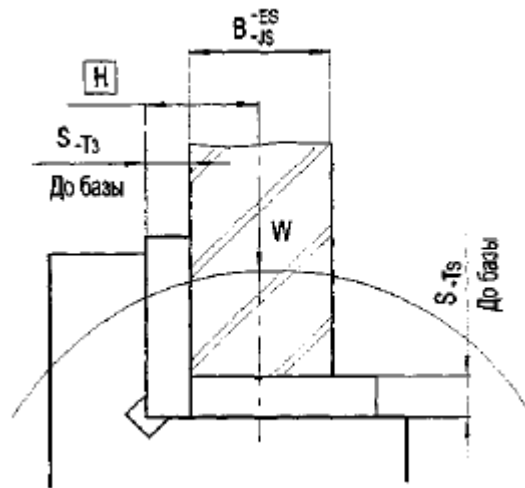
Схема налаштування інструмента для фрезерування шпонкового паза
